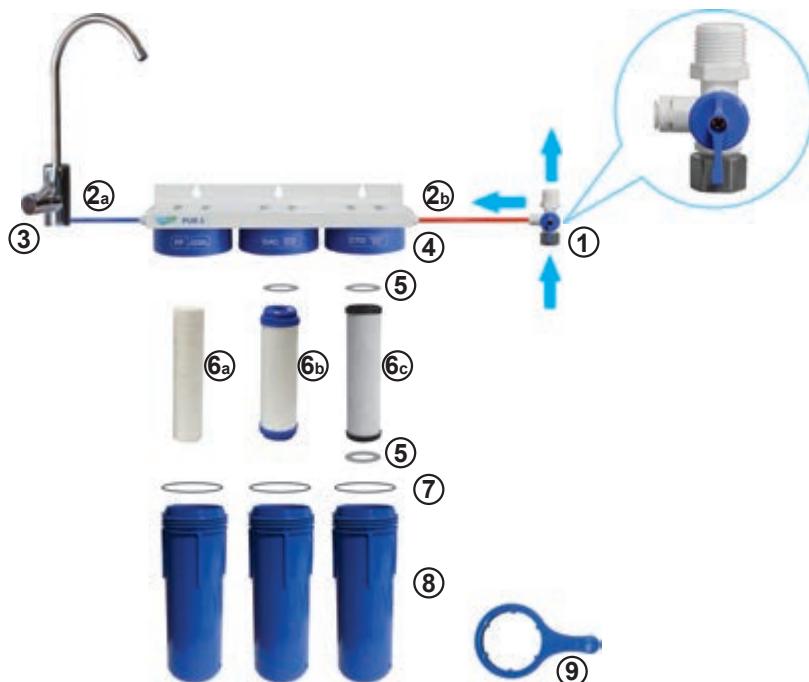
Schema di montaggio del sistema PUR 3 (da destra verso sinistra)
